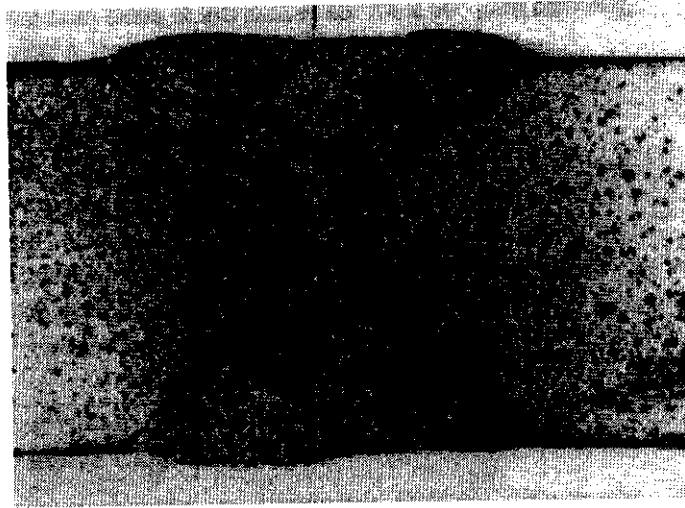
Soldadura MIG en varias pasadas realizada en A356/SiC/20p (109)
